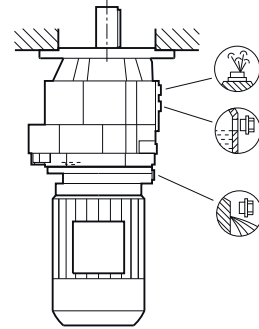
Düz dişli için montaj konumları DF/ZF Flanşlı model ve gövde flanşlı DZ/ZZ, Boyut 39
